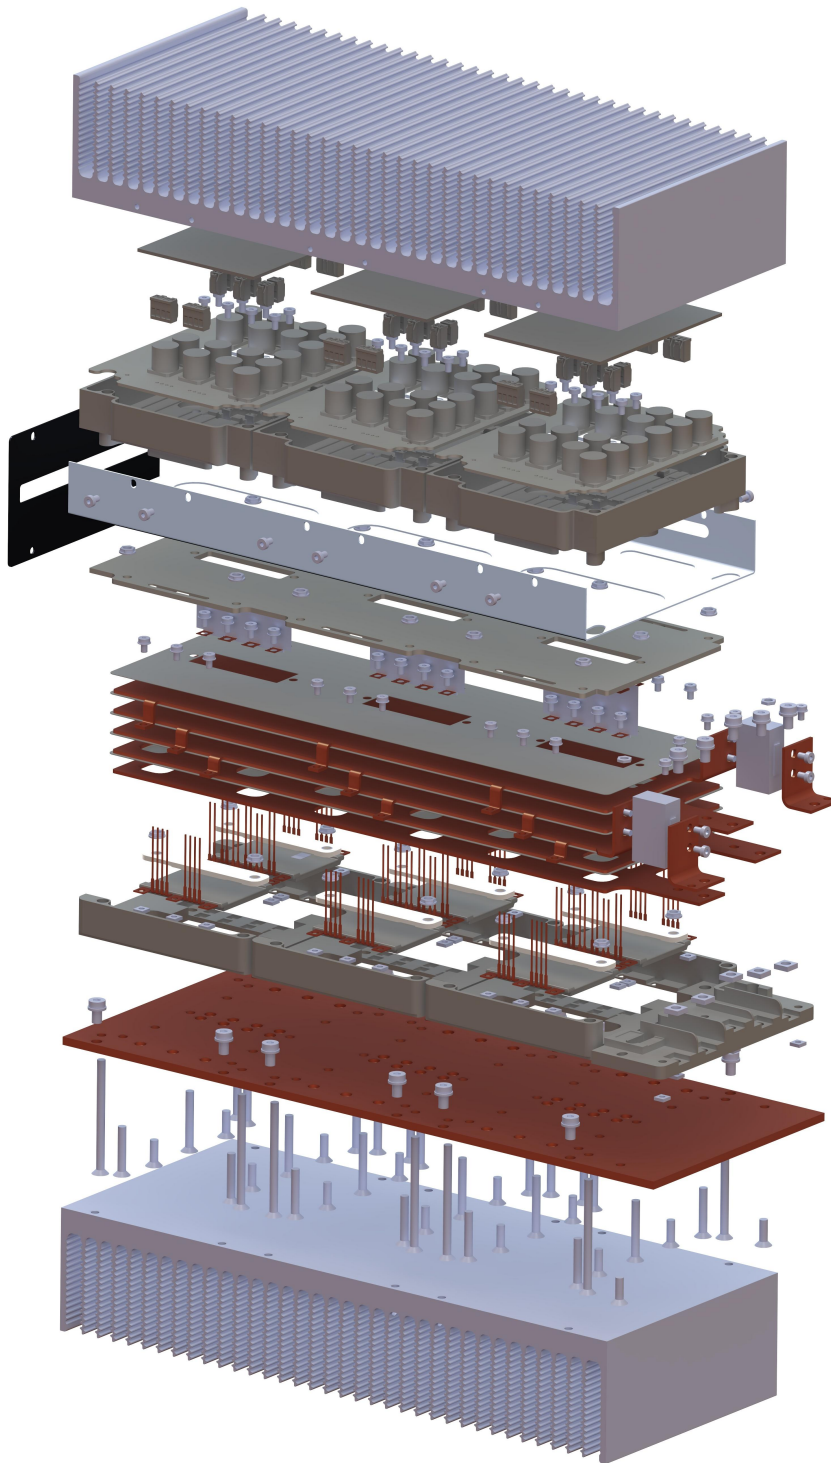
Explosionszeichnung des 15 kVA-Umrichters [152]
